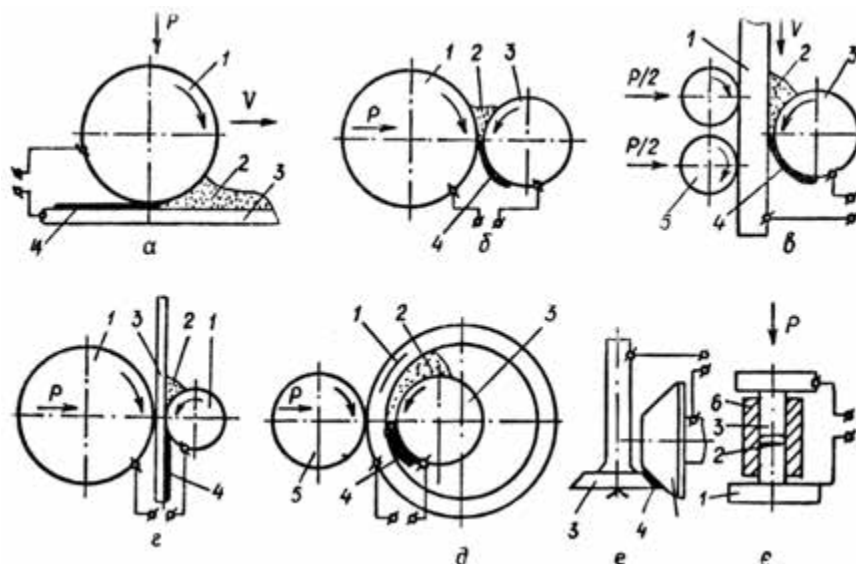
Схеми електроконтактного напівання металевих порошків: а, б, в, г, д, е, є - варіанти; 1 – контактний ролик електрод; 2 – металічний порошок; 3 – деталь; 4 – напечений шар порошку; 5 – натискний ролик; 6 – форма
